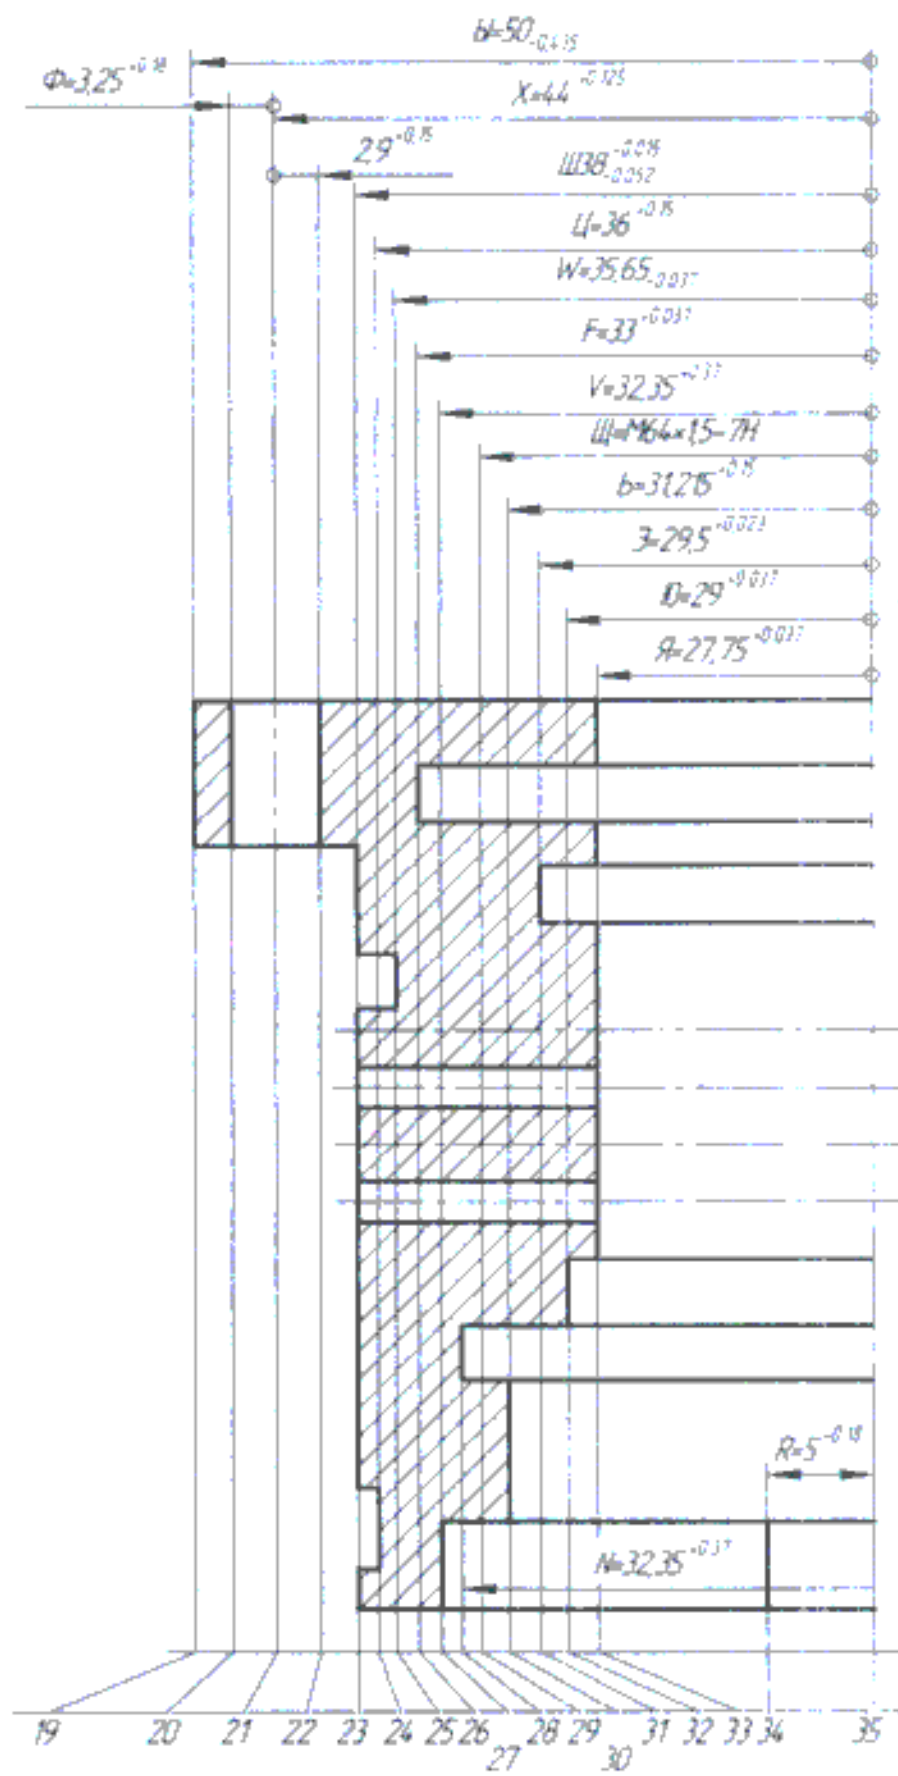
Преобразованный чертеж детали по диаметральным размерам
